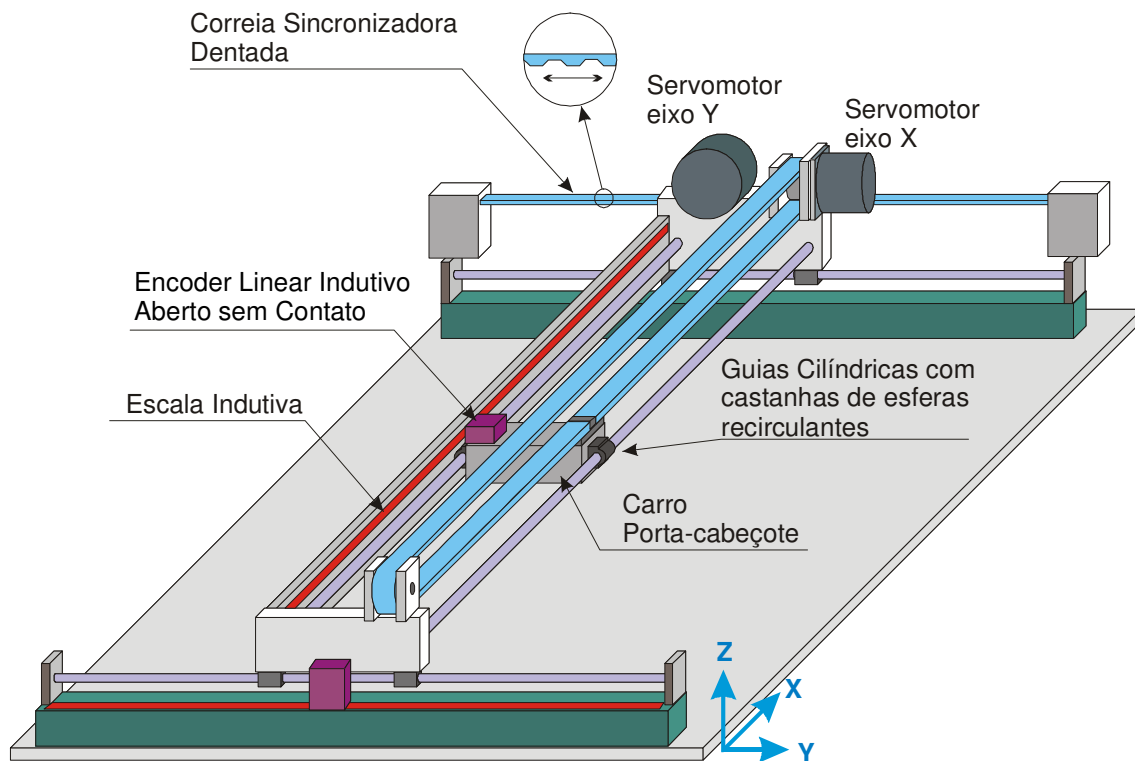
Esquema dos componentes mecânicos definidos para o conjunto impressor.
